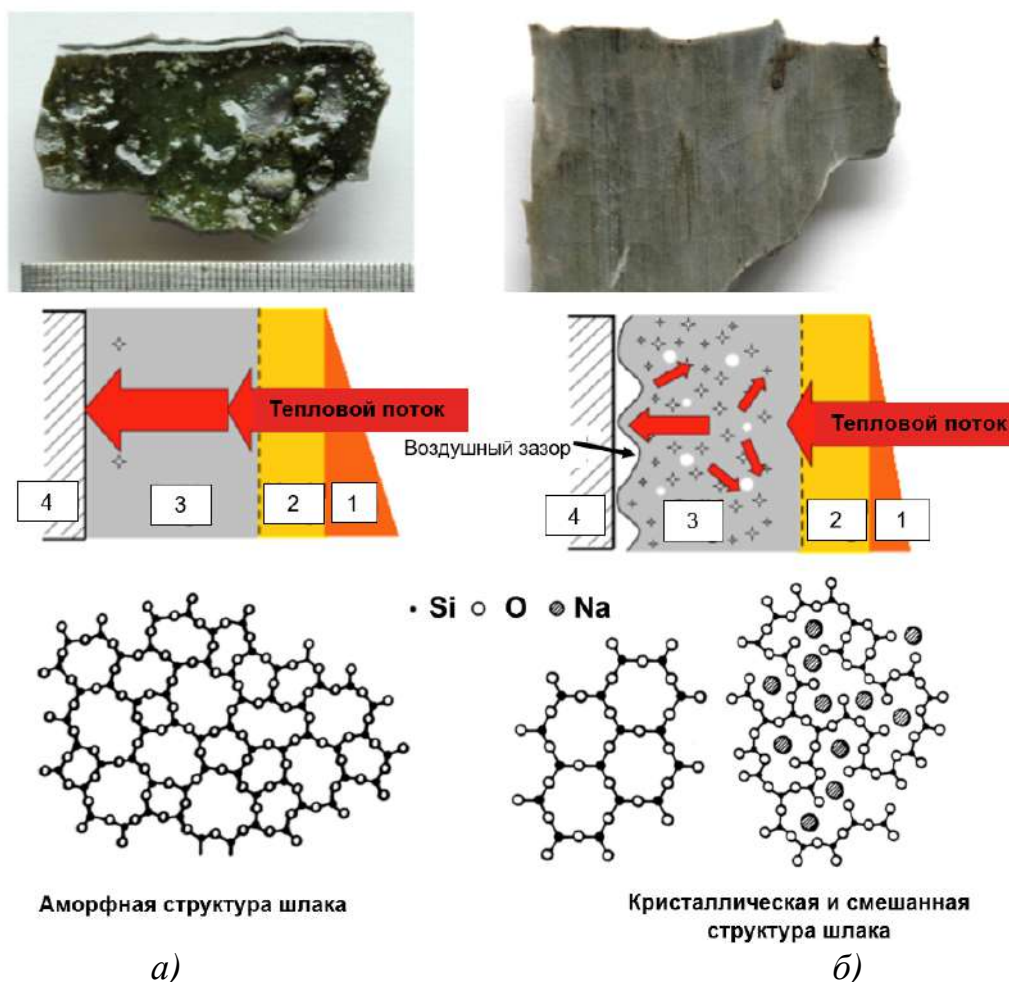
Схема передачи тепла для аморфного (а) и кристаллического (б) шлаков и внешний вид твёрдых шлаков; 1 – затвердевшая оболочка слитка; 2 – жидкий слой шлака; 3 – твёрдый слой шлака; 4 – медный кристаллизатор УНРС
